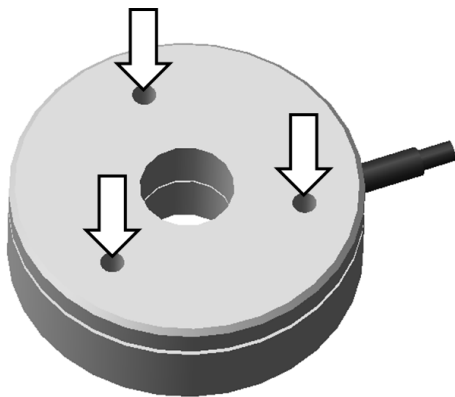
Montagebohrungen in der Bewegungsplattform des S-303
